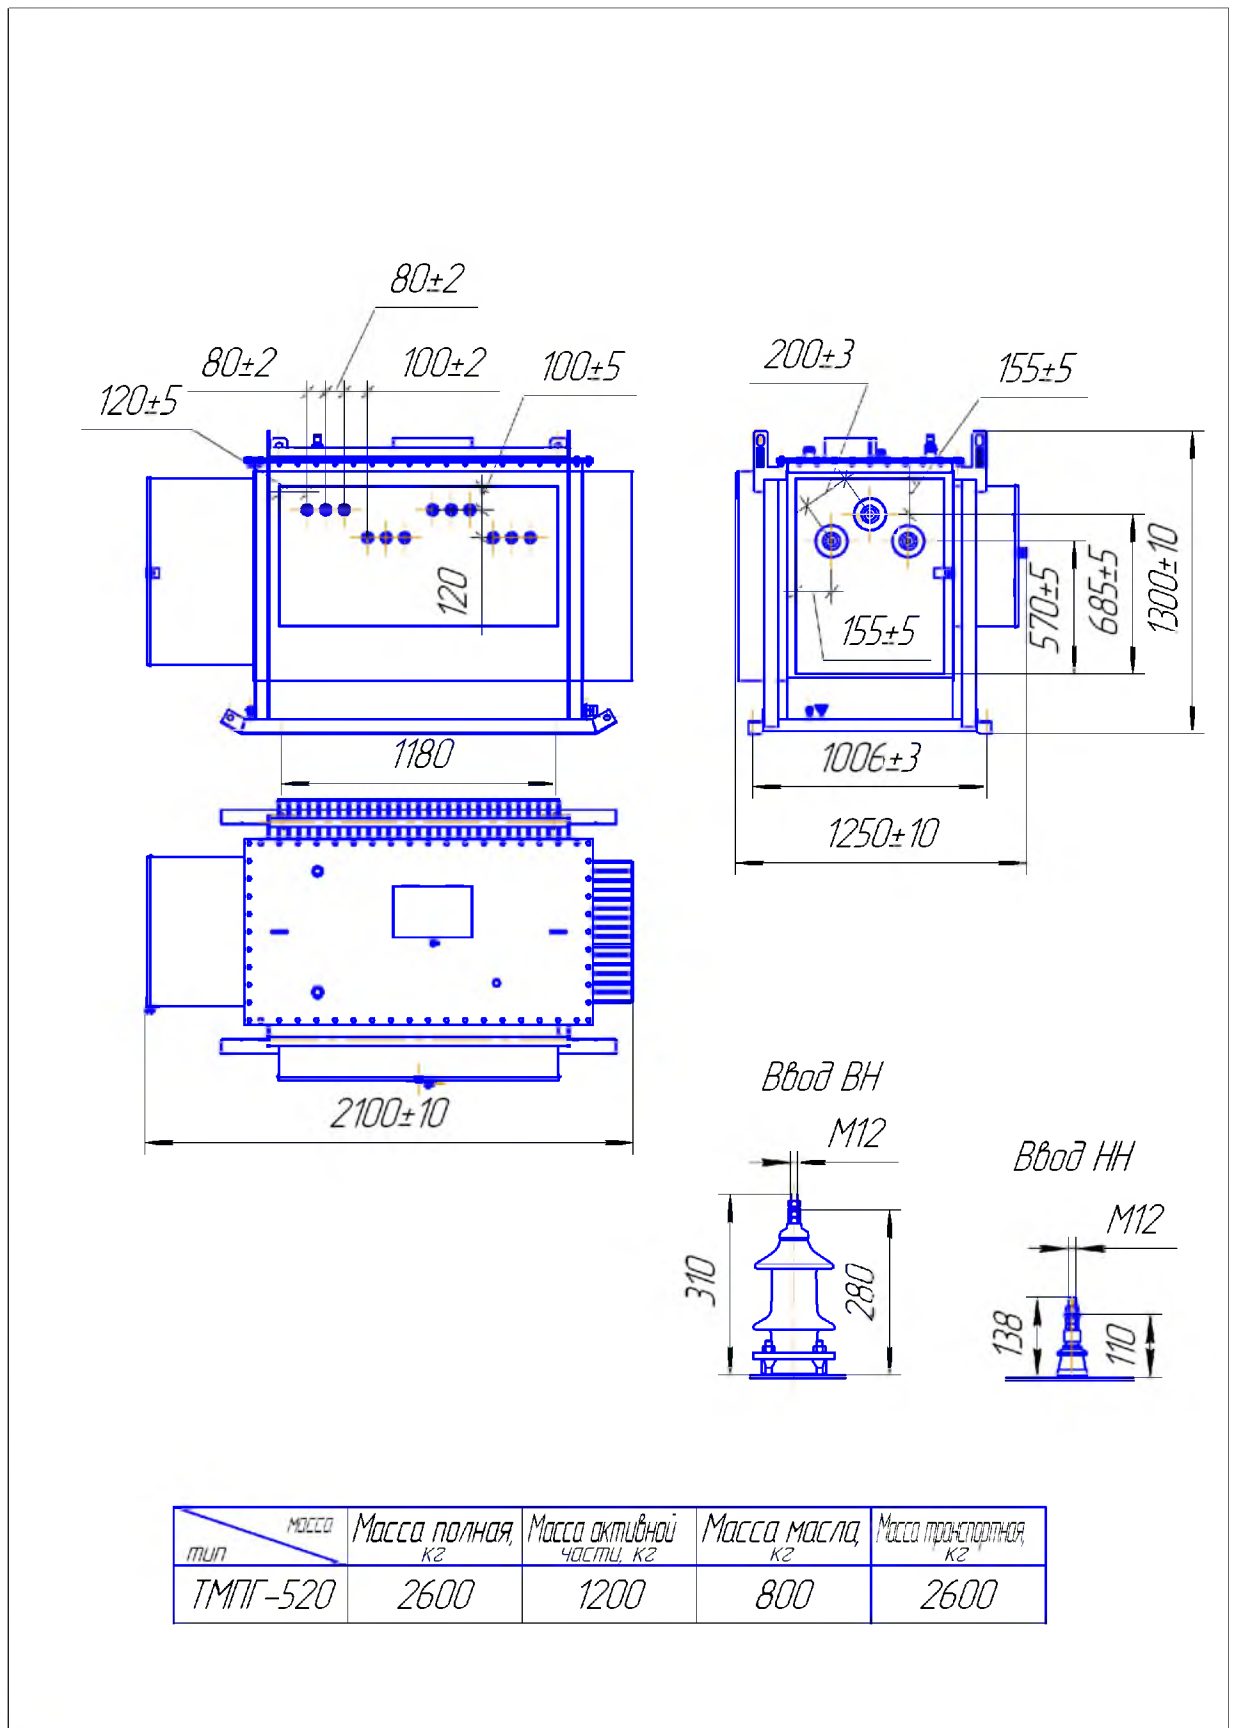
Габаритные, установочные и присоединительные размеры трансформаторов ТМПГ-СЭЩ-520
